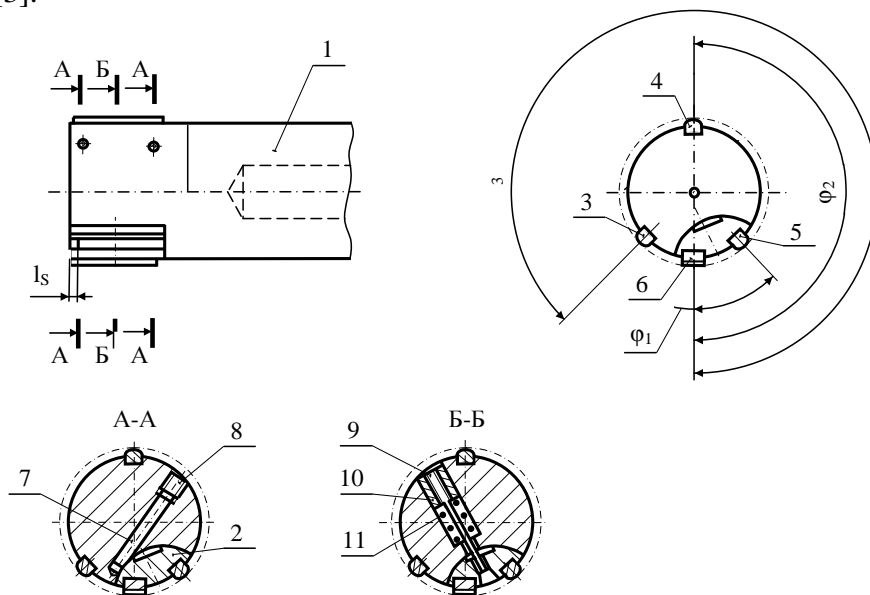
Схема АВР для обработки отверстий: 1 – корпус; 2 – поворотный блок; 3 и 4 – боковой и опорный направляющие элементы; 5 и 6 – направляющий и абразивный элемент, установленные в поворотном блоке; 7 – регулировочные клинья; 8, 9 – винты; 10 – резьбовая втулка; 11 – пружина
